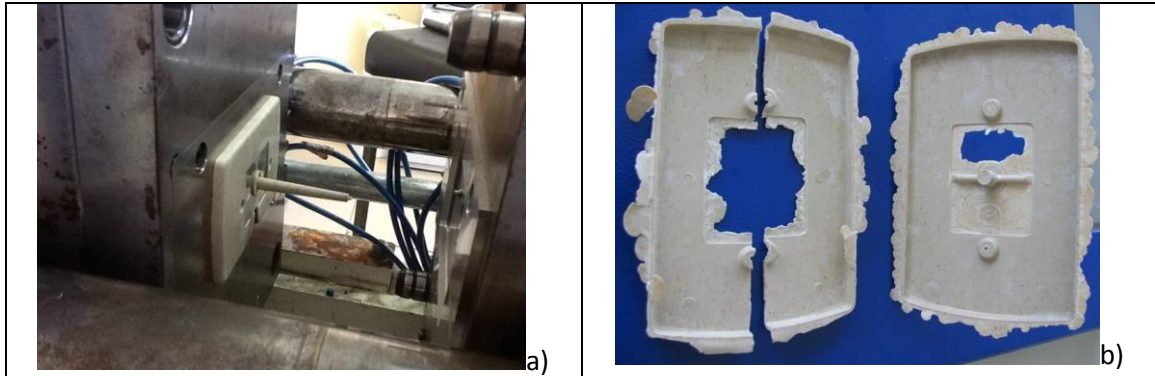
a) Protótipo do dispositivo elétrico após moldagem ilustrando dificuldades de extração da peça do molde b) Fraturas em linhas de solda.
